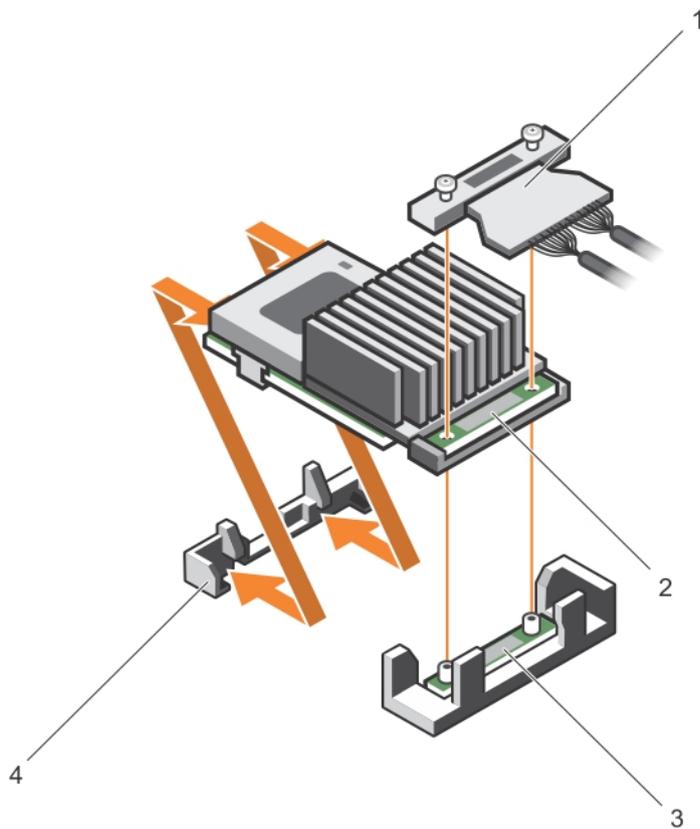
Como remover e instalar a placa controladora de armazenamento integrado
